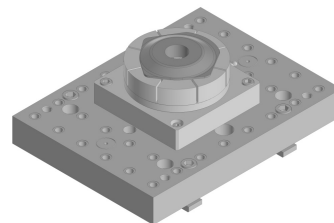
3D модель станочного приспособления для установки крышки
